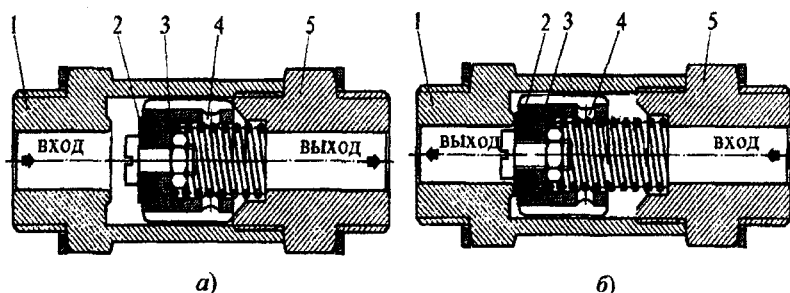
Обратный клапан, *а* – открыто, *б* – закрыто. 1 – корпус, 2 – кольцо уплотнительное, 3 – поршень, 4 – отверстие радиальное, 5 – крышка
